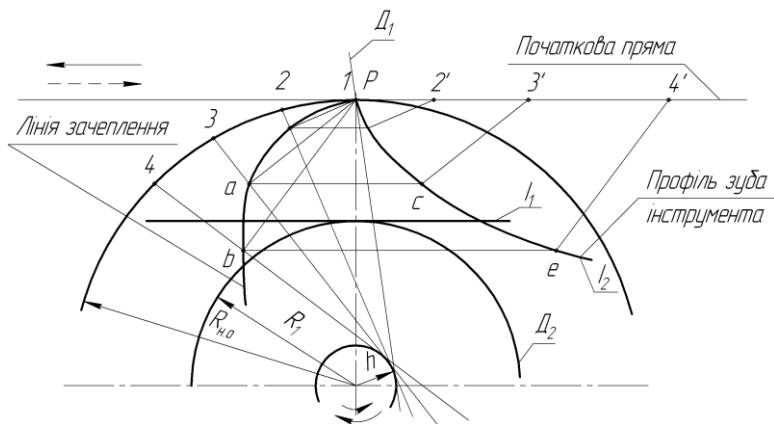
Графічне профілювання зуба черв'ячної фрези для обробки шліцьового валу
